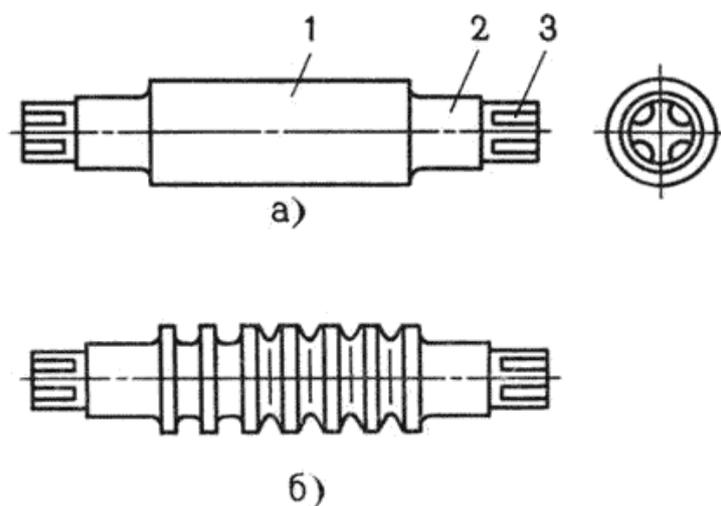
Прокатные валки: а – гладкий ; б – калиброванный
